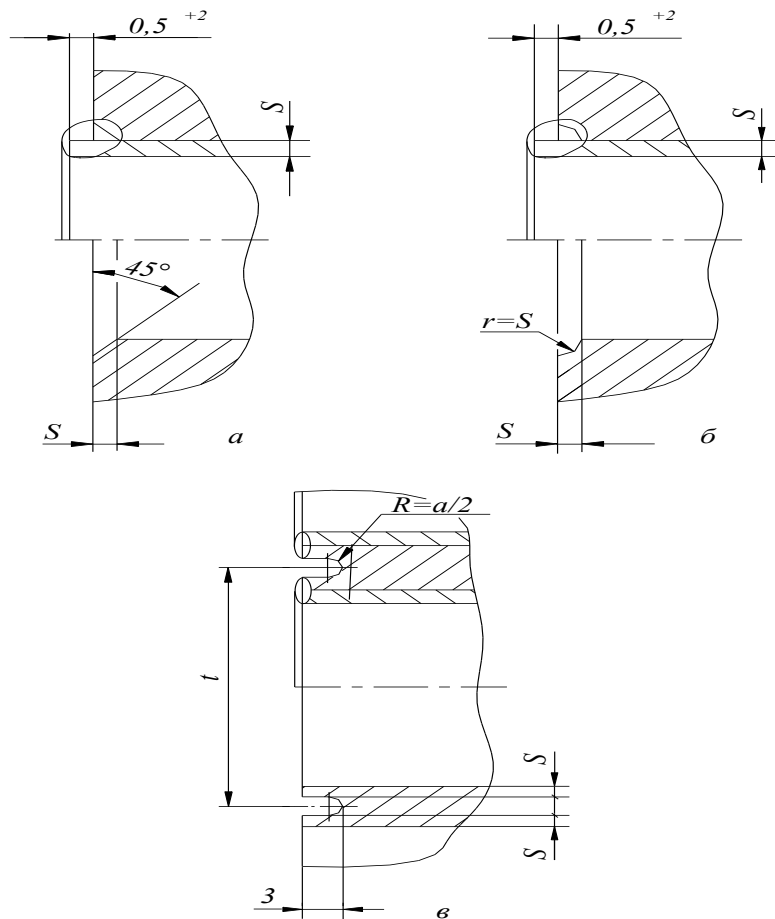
Типи зварки труб із трубними решітками.
